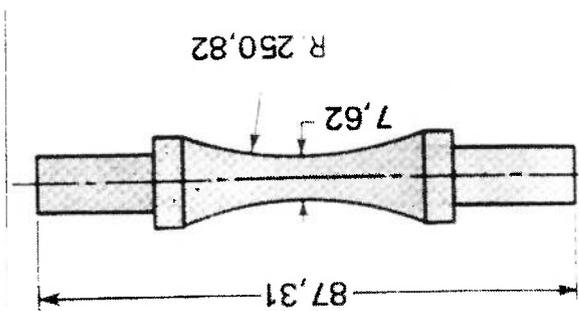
Corpo de prova para a máquina de teste de flexão rotativa de R. R. Moore⁽¹⁾
